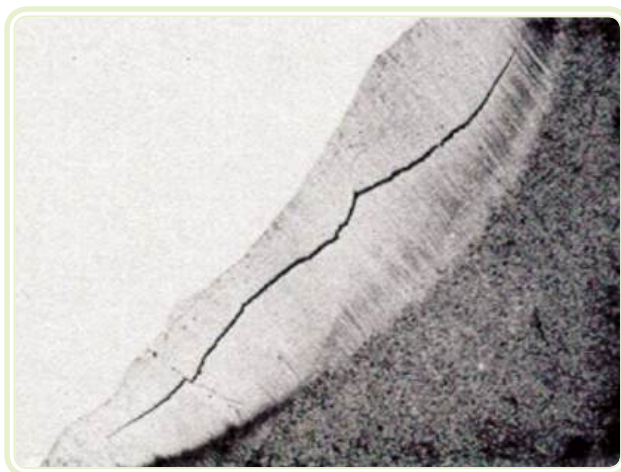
Trinca a frio sob o cordão na soldagem de aço baixa liga
